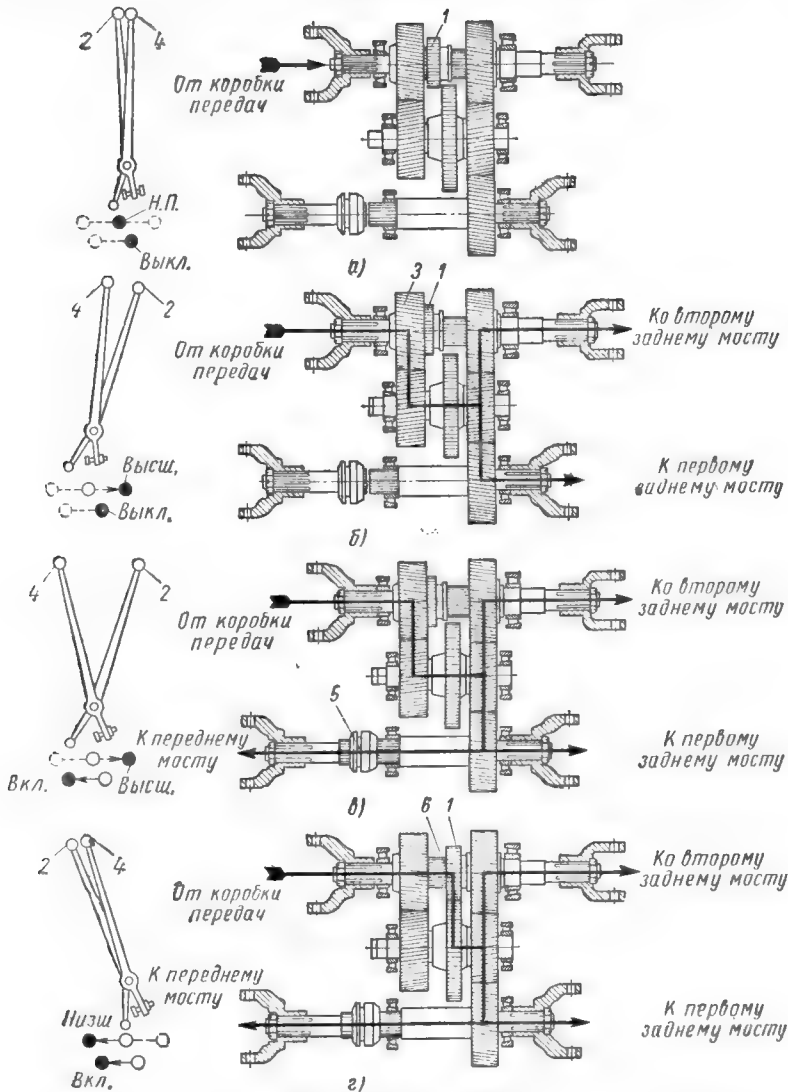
Раздаточная двухступенчатая коробка автомобиля ЗИЛ-151.
